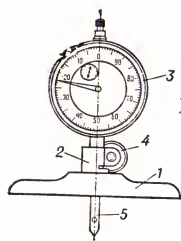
Индикаторный глубиномер: 1 — основание; 2 — державка; 3 — индикатор; 4 — винт для крепления индикатора; 5 — сменный измерительный стержень.
